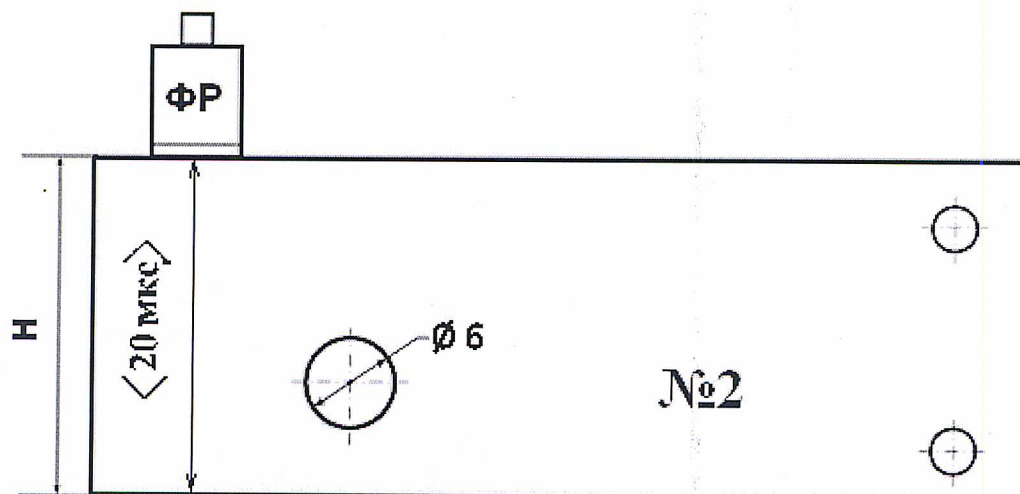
Контрольный образец №2 из комплекта КОУ-2
